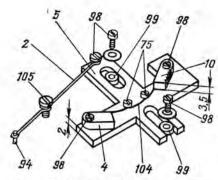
Тормозное устройство: 2 — рычаг тормоза, проволока сталывая класса II диаметром 0.8 мм; 4 — колодка тормоза подающего узла, резина; 5 — плапка тормоза, Д16A-Т; 10 — колодка тормоза приемного узла, Л62-Т; 75 — вилы М2-Х 3, 2 шт.; 98 — винт М2-Х 5, 5 шт.; 99 — втулка, ЛС59-1, 2 шт.; 104 — пружина, проволока стальная класса II диаметром 0,5 мм; 105 — винт М3-Х 10.
